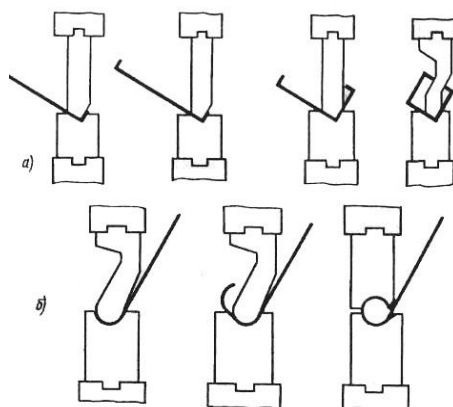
Схема гибки профилей на прессах с поступательным движением ползуна
